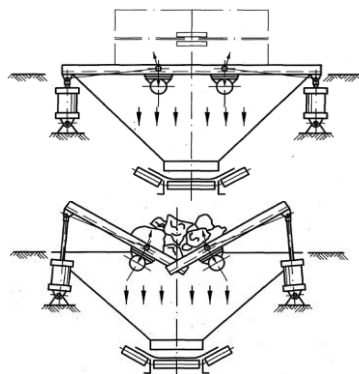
Способ и устройство для выбивки формовочной смеси из опок и измельчения образующихся при этом комьев смеси [34]
